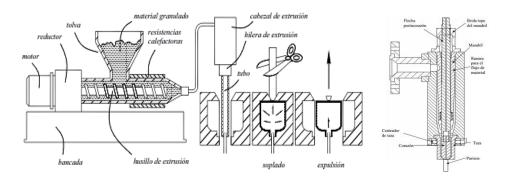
Elementos de la máquina de soplado a) (derecha) máquina de soplado b) (izquierda) cabezal de extrusión
